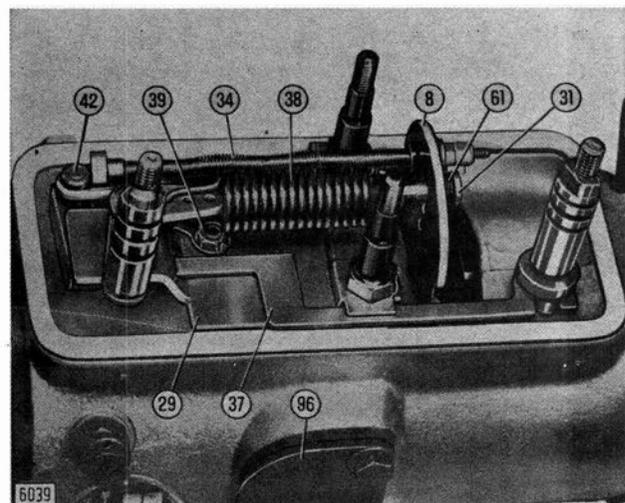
Vue du régulateur de vitesse, le couvercle étant déposé.
